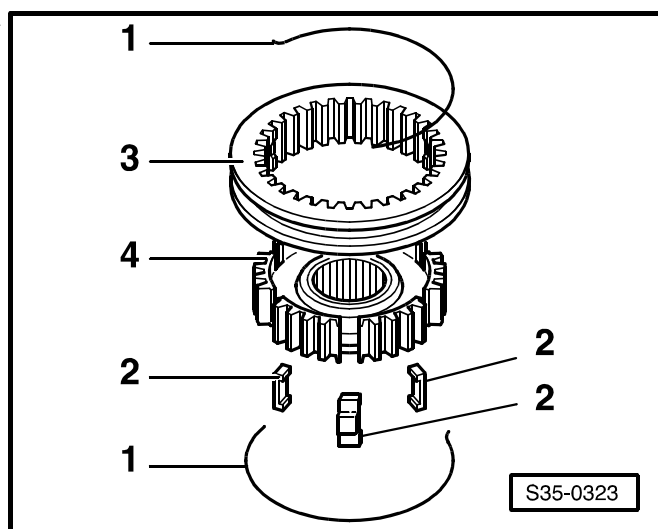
Сборка скользящей муфты и каретки синхронизатора 5-ой и 6-ой передач
